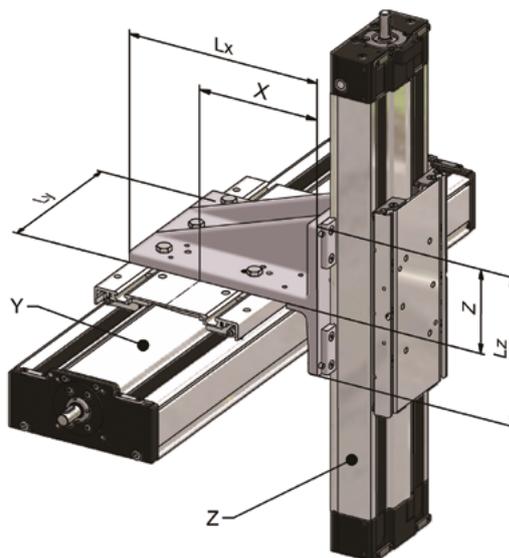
Winkelverbindung Y – Z – Achs – System, Profilmontage
